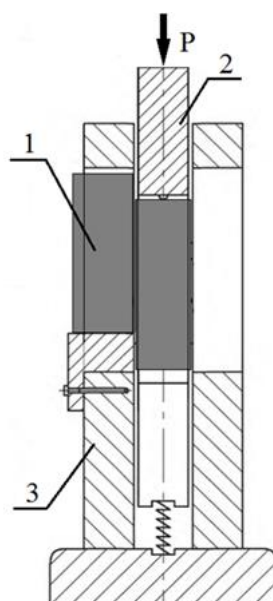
Схема приспособления для фиксации образцов и передачи на них нагрузки: 1 – образец; 2 – подвижная часть приспособления, передающая нагрузку на образец; 3 – неподвижная часть приспособления, фиксирующая образец
